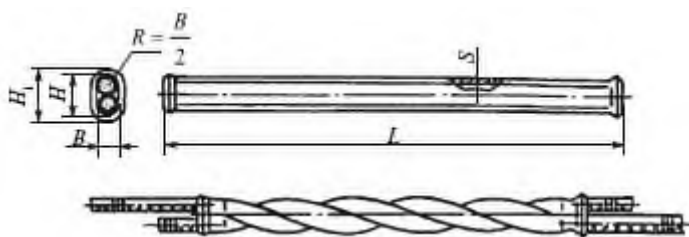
Соединительный овальный зажим типа СОАС для алюминиевых и сталеалюминиевых проводов.
